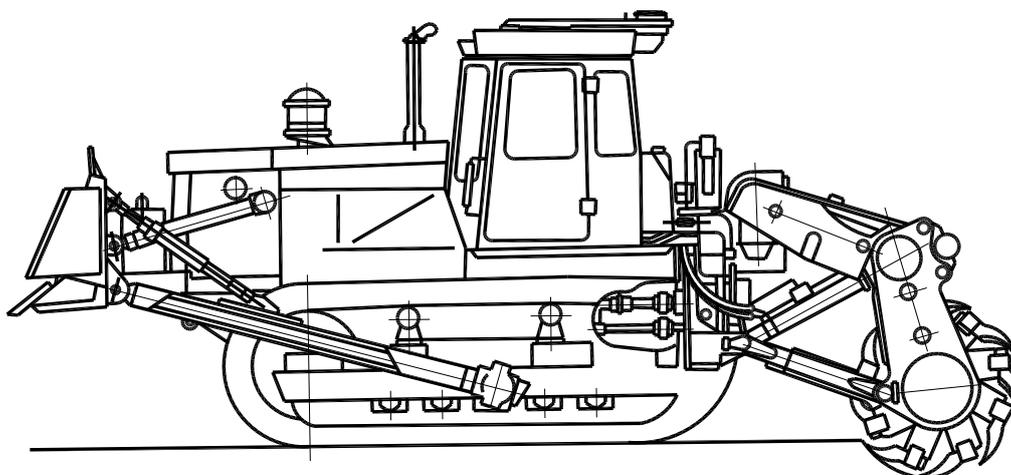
Машина для послойного фрезерования ДП–31АХЛ
